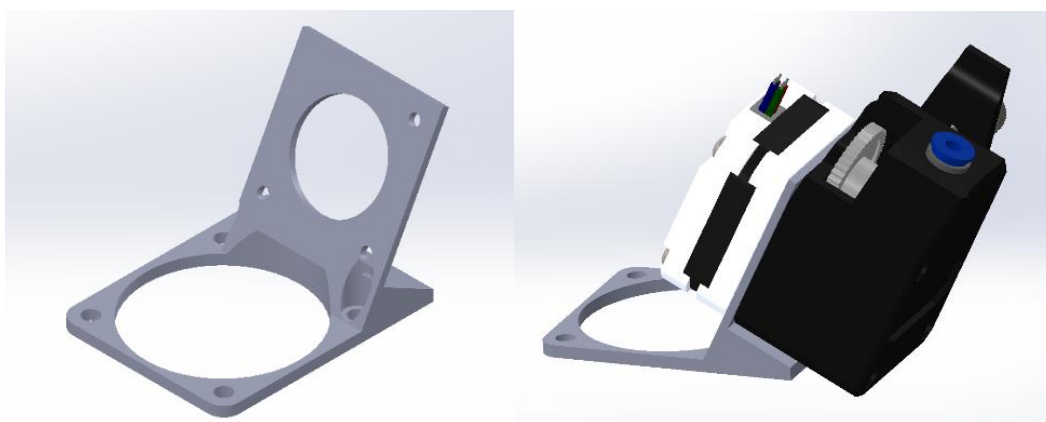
À esquerda o suporte da extrusora *direct drive*; à direita o conjunto assembledo.
